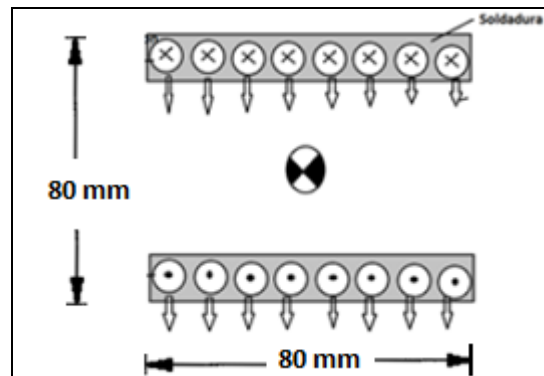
DIMENSIONAMIENTO DEL CORDÓN DE SOLDADURA EN EL MONTAJE.
